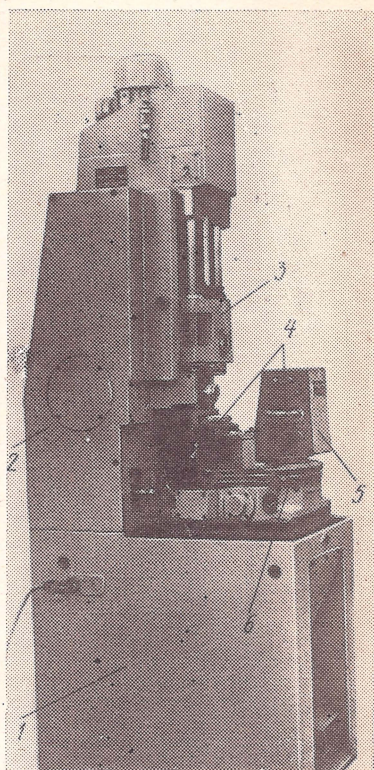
Вертикальный внутридоводочный многопозиционный станок 3820Д
